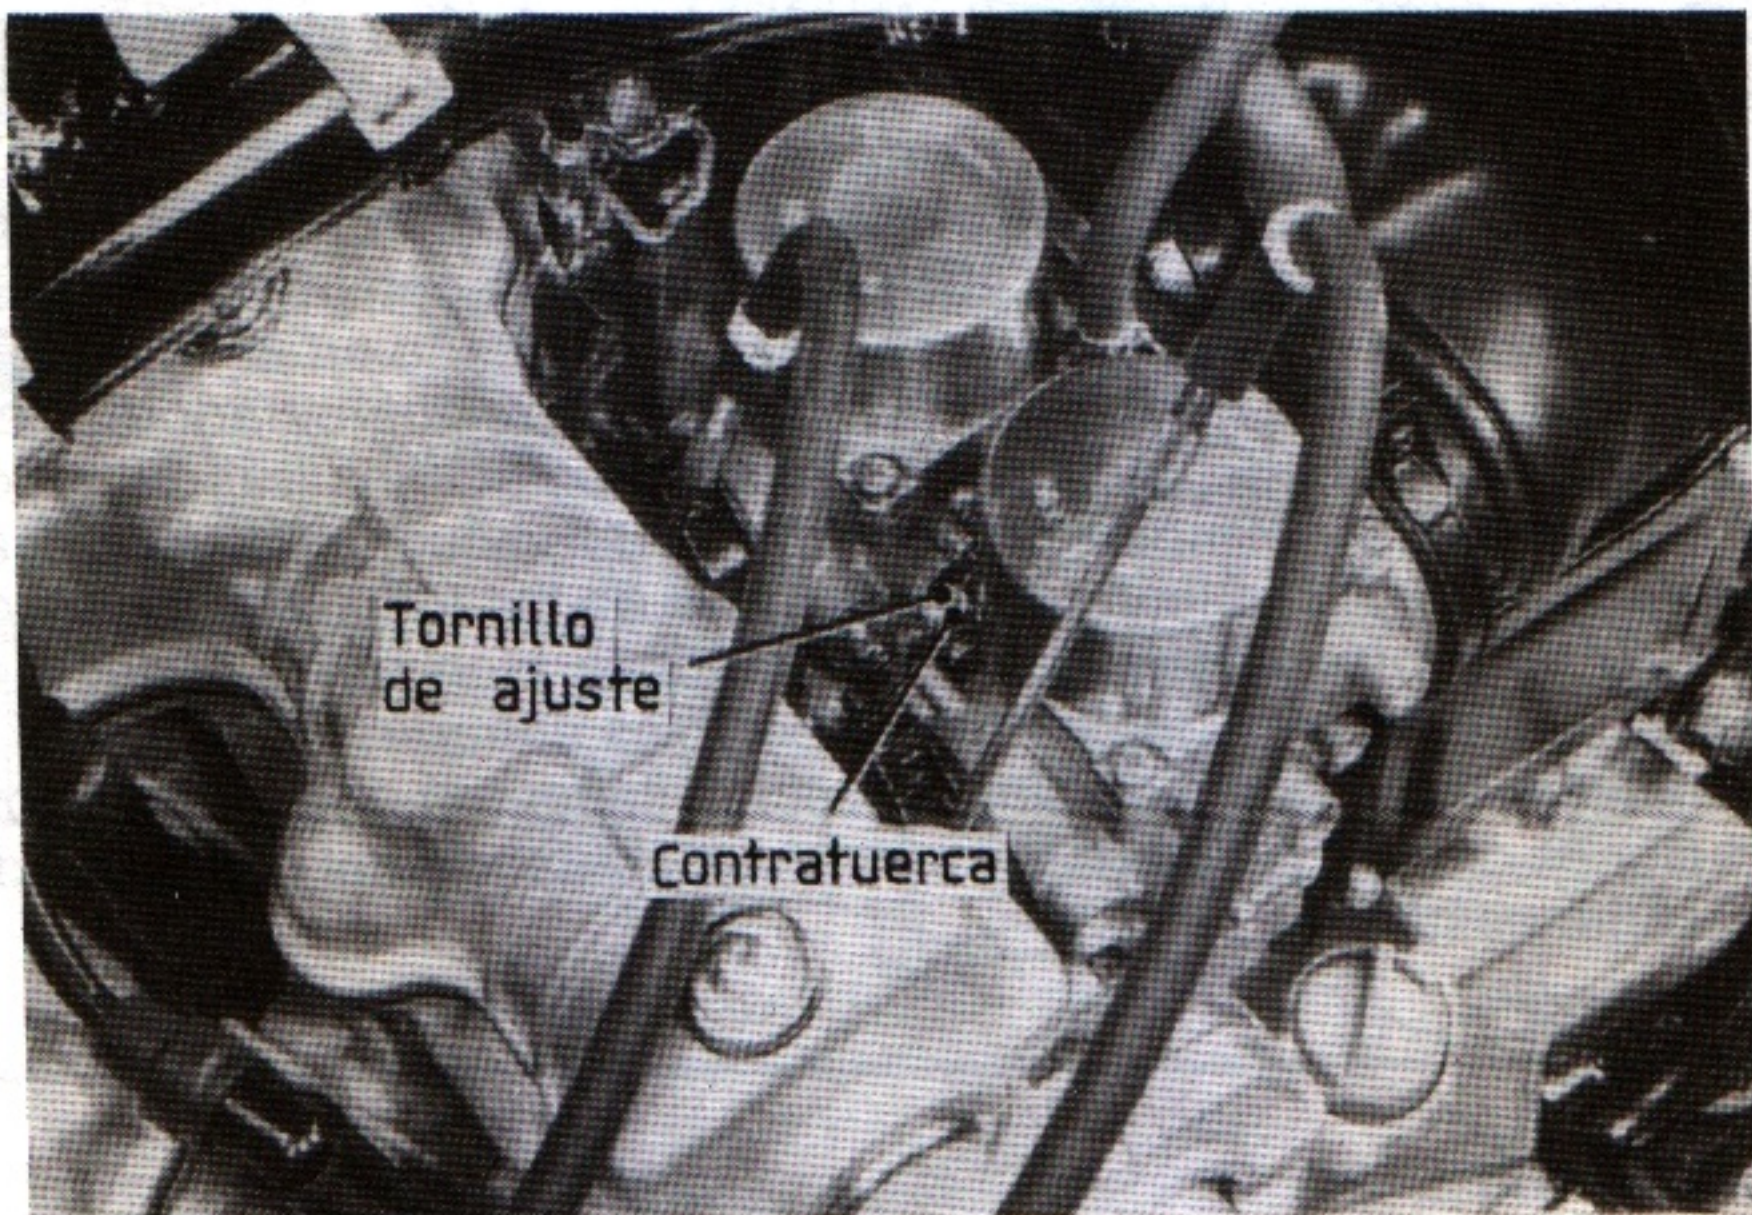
Accionando el tornillo de ajuste de la sincronización y su contratuerca hay que conseguir restablecer el valor del carburador patrón en el carburador que estamos ajustando.
